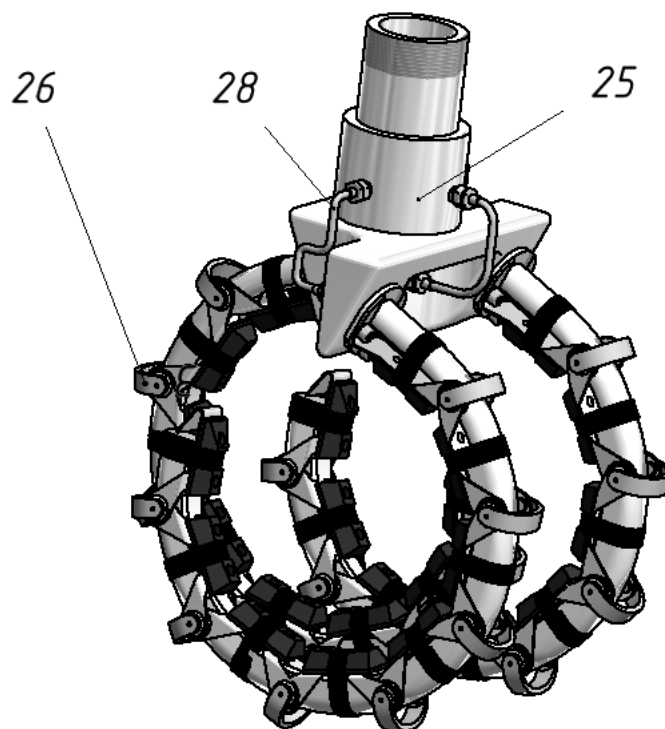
Захватний пристрій для маніпулювання довгими об'єктами
